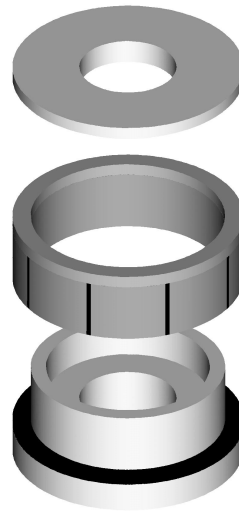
Prinzipieller Aufbau eines Motors mit Dehnungswelle
